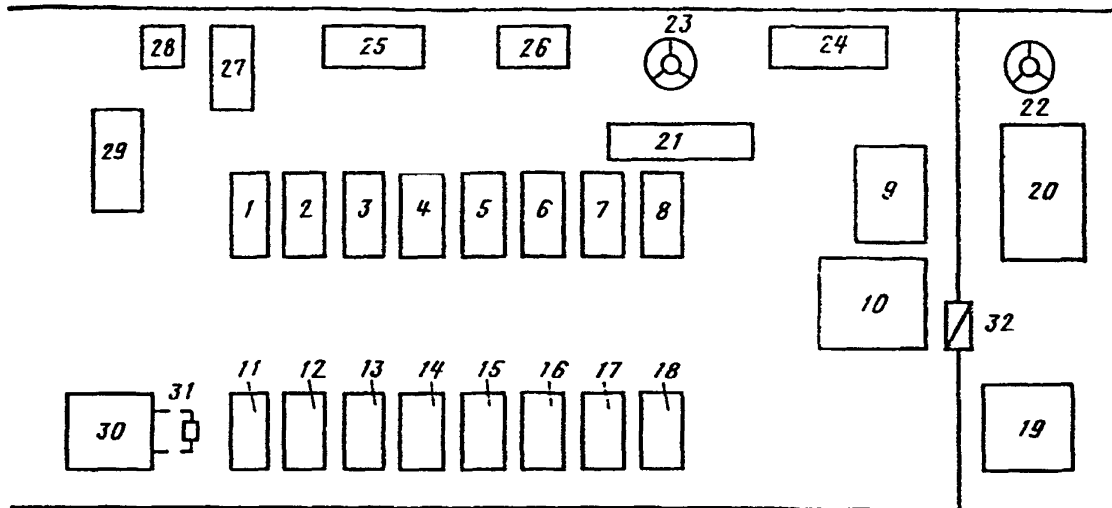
Типовая схема организации рабочего места сборки коробки передач:
